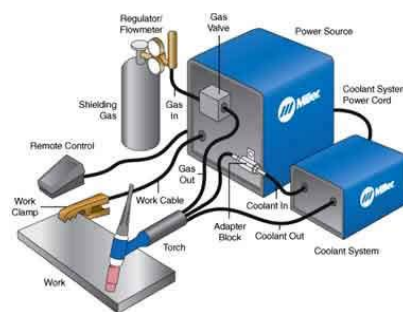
Equipamiento básico para soldadura TIG o GTAW
